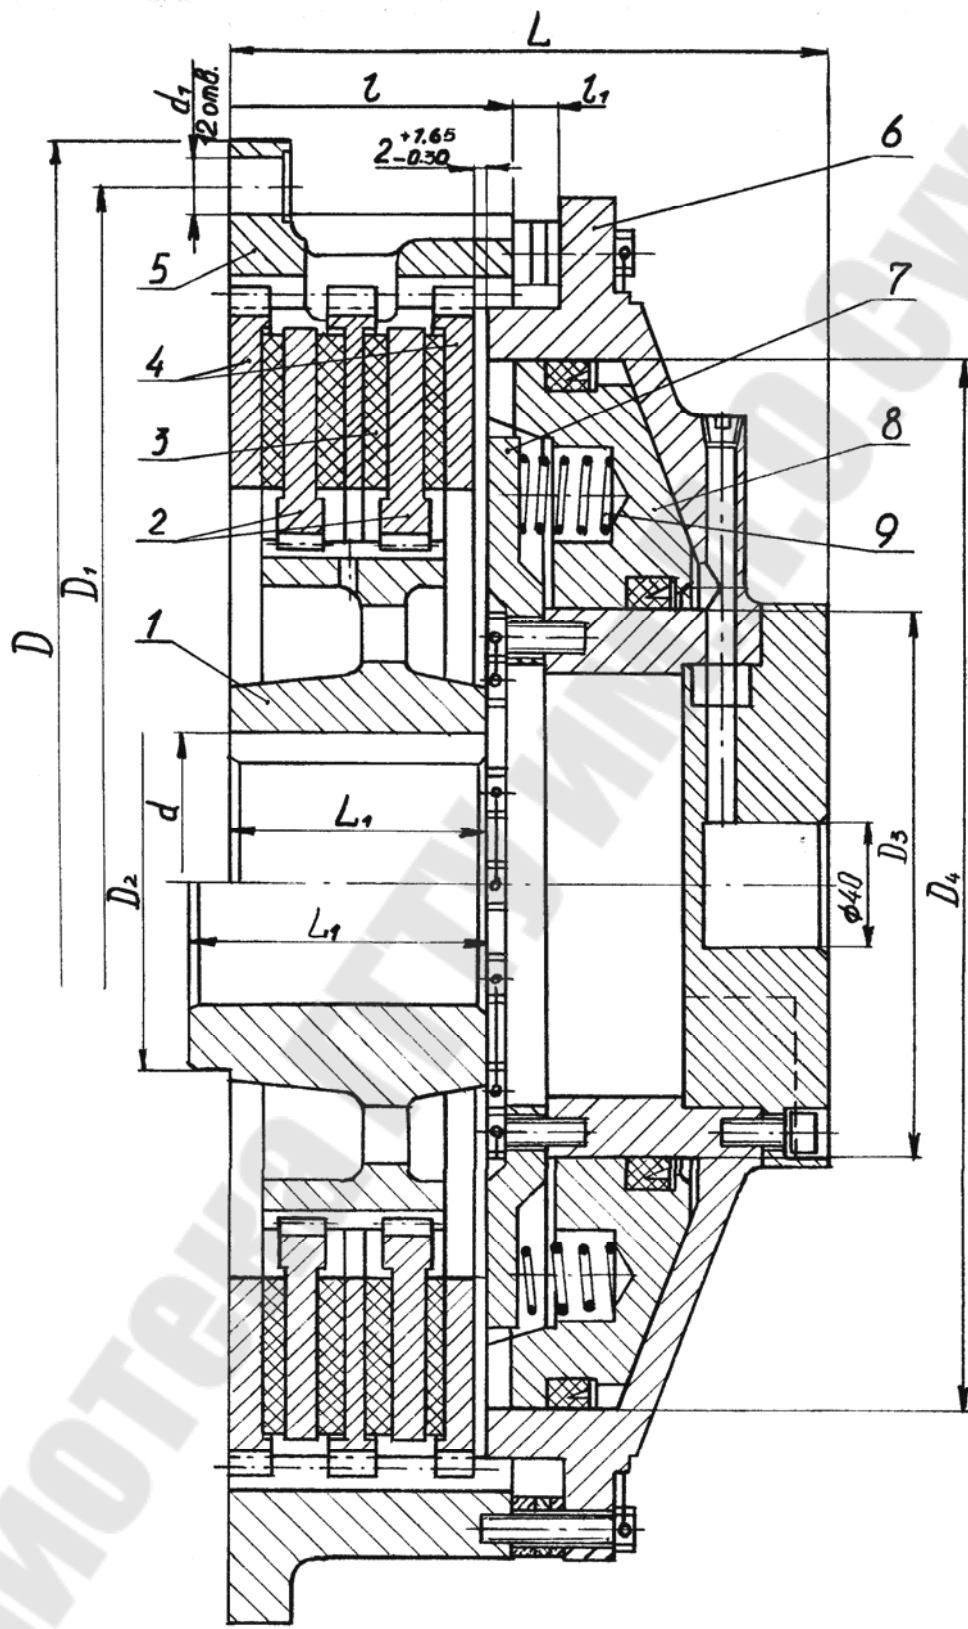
Габаритные и присоединительные размеры муфт
